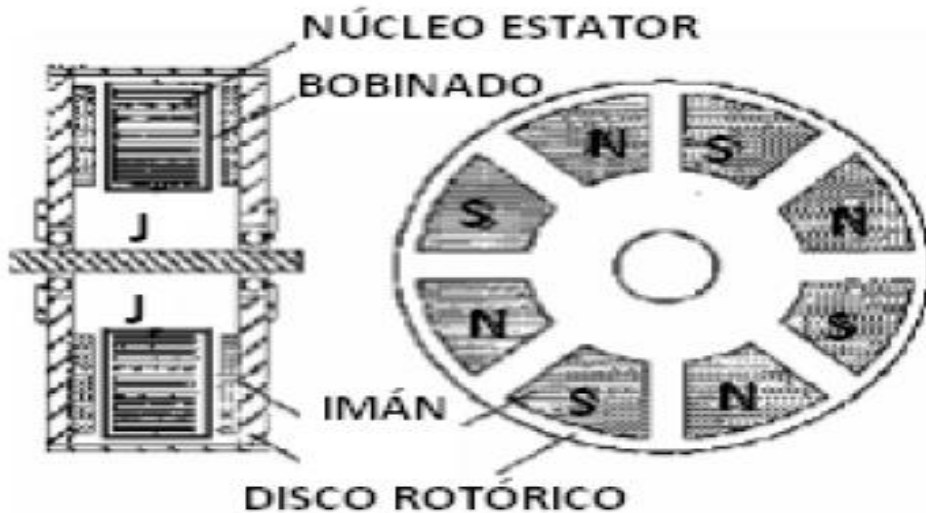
Máquina axial con 2 rotores exteriores de imanes (AFPM).
